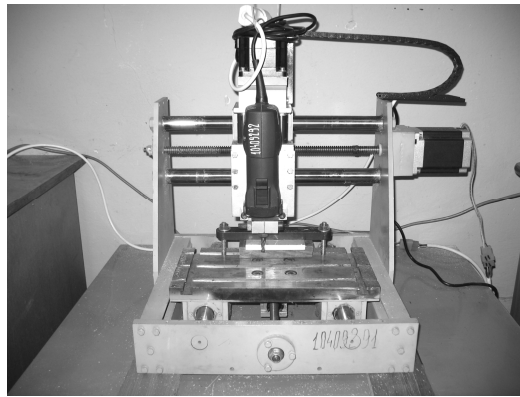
Гравірувально-фрезерний верстат з ЧПУ
